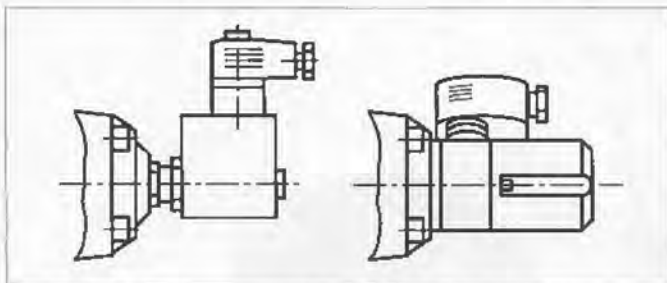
Электронный или путевой контроль: слева – индуктивный бесконтактный выключатель, справа – механический контактный выключатель
